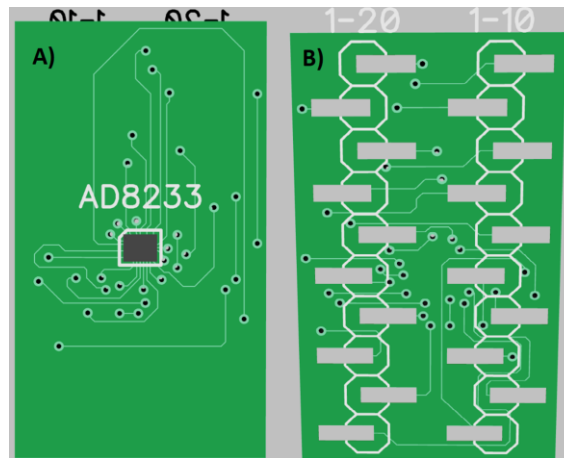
Vista 3D del Adaptador SMD-DIP en PCB del chip AD8232
